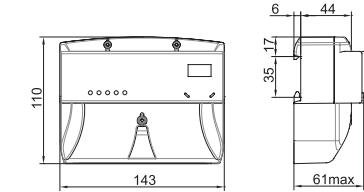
Габаритные и присоединительные размеры счётачиков габарита корпуса 6.
